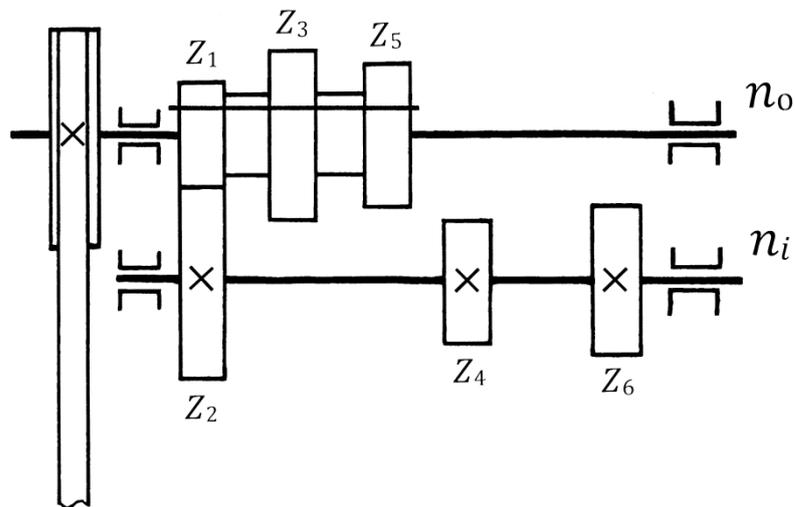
Передача цилиндрическими зубчатыми колёсами
